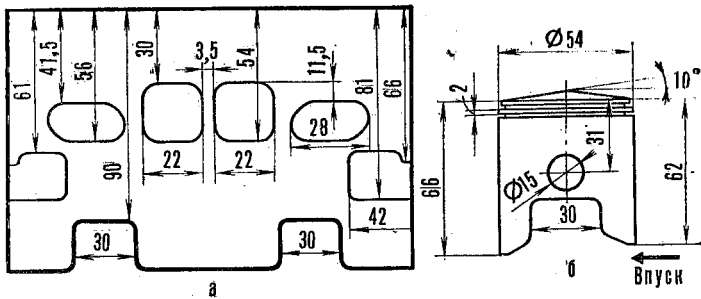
Развертка цилиндра (а) и поршень (б) двигателя А. Савельева
